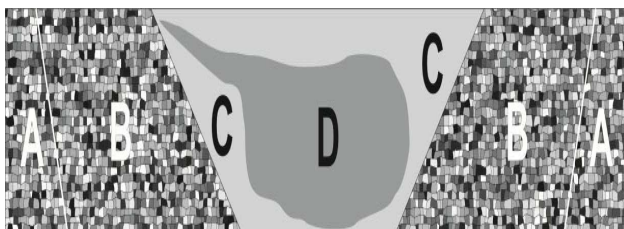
Clasificación de las estructuras en la soldadura FSW. Fuente: Threadgill (1997).
